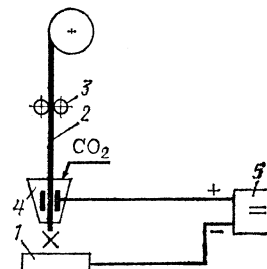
Принцип сварки: 1 — изделие; 2 — электродная проволока; 3 — ролик механизма подачи электродной проволоки; 4 — газовое сопло; 5 — источник питания
